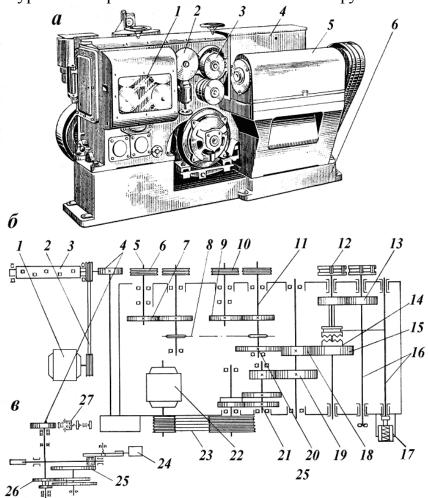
Станок для одновременной правки и резки арматурной стали с непрерывной подачей: a – общий вид: δ – кинематическая схема
